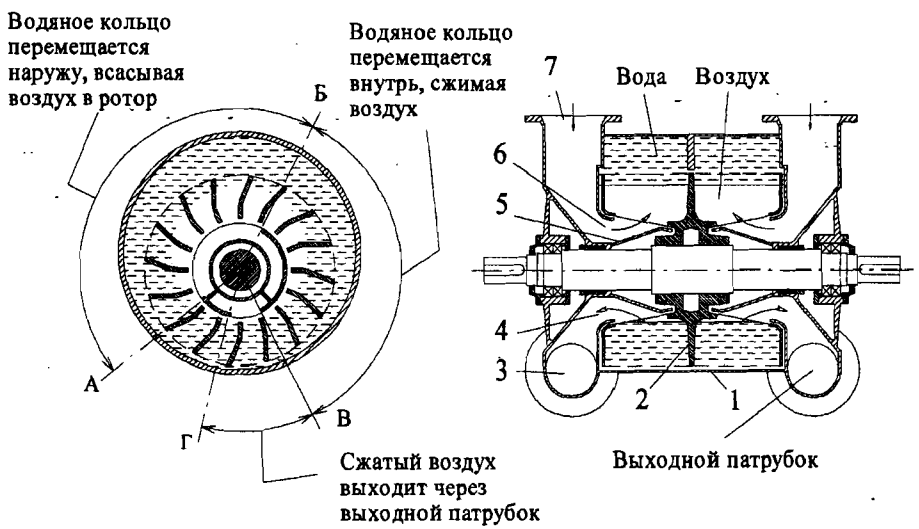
Схема водокольцевого вакуумного насоса: 1 – корпус; 2 – колесо; 3 – нагнетательный патрубок; 4 – нагнетательное окно; 5 – неподвижный конус; 6 – всасывающее окно; 7 – всасывающий патрубок
